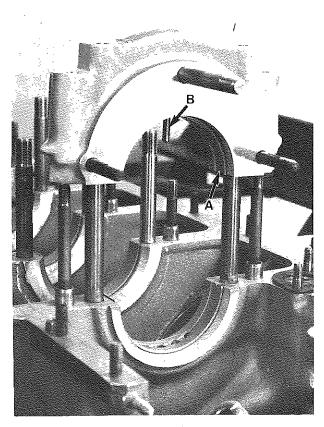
A) Cuscinetto - B) Frangiolio A) Bearing - B) Oil breaker
